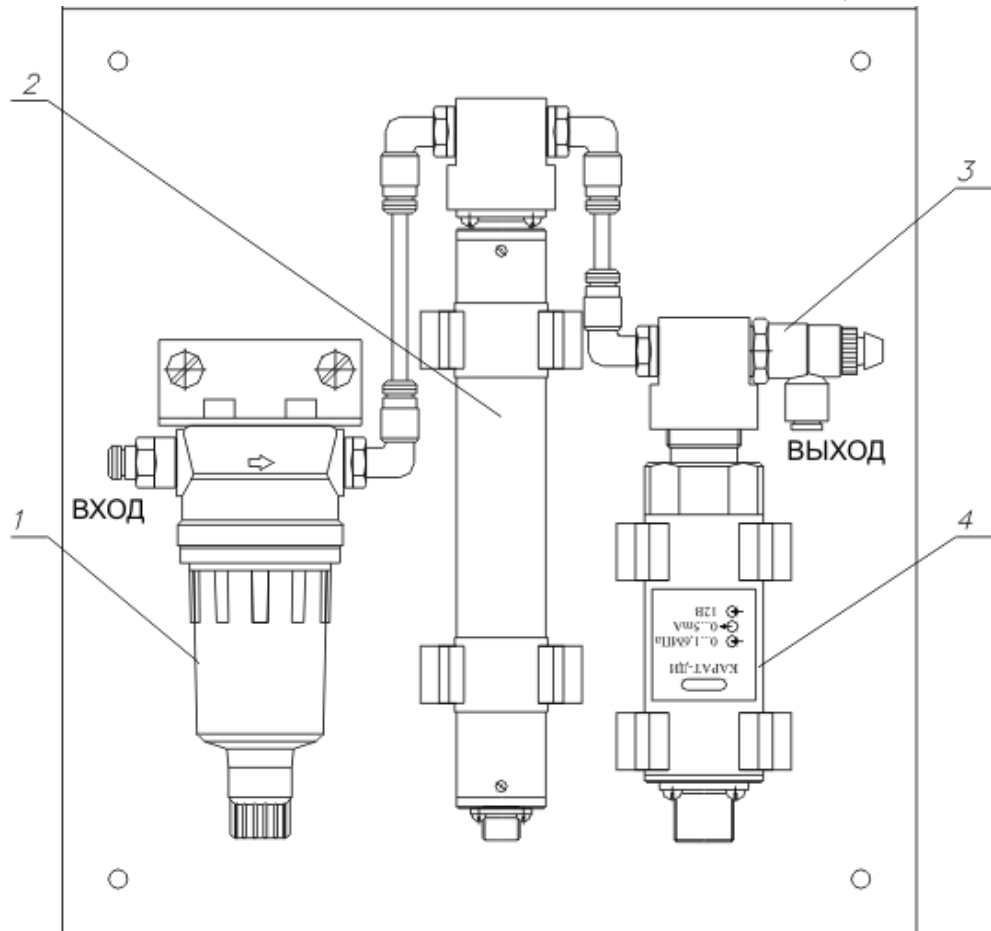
Стенд системы пробоподготовки газов СПГ-3 и СПГ-3М
